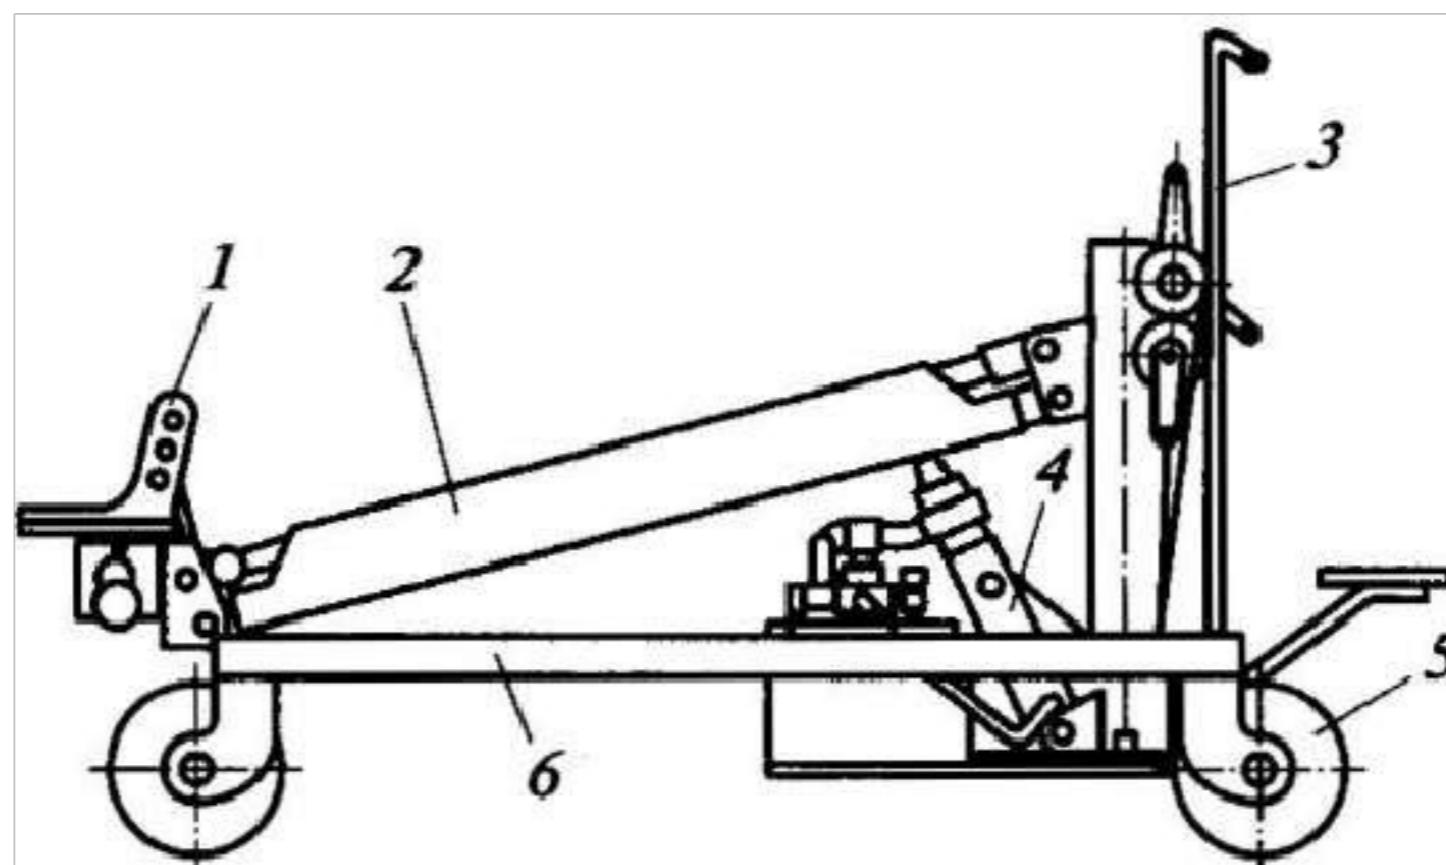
Тележка для снятия и постановки рессор: 1- подхват для рессор; 2 — стрела; 3 — рукоятка; 4 — гидроцилиндр; 5— колесо; 6 — продольная балка
